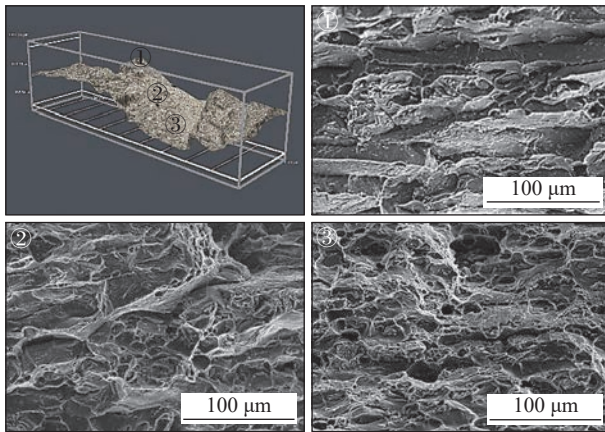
脉冲 VP-TIG 焊接接头 2219 侧断口形貌
